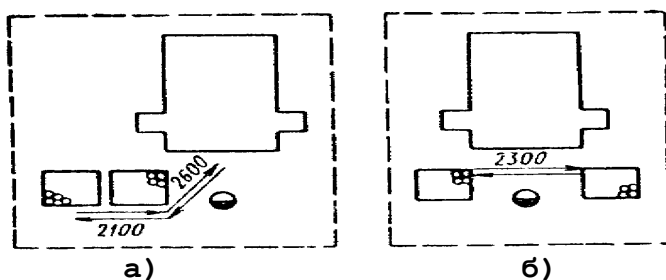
Схемы вариантов планировки рабочего места фрезеровщика
